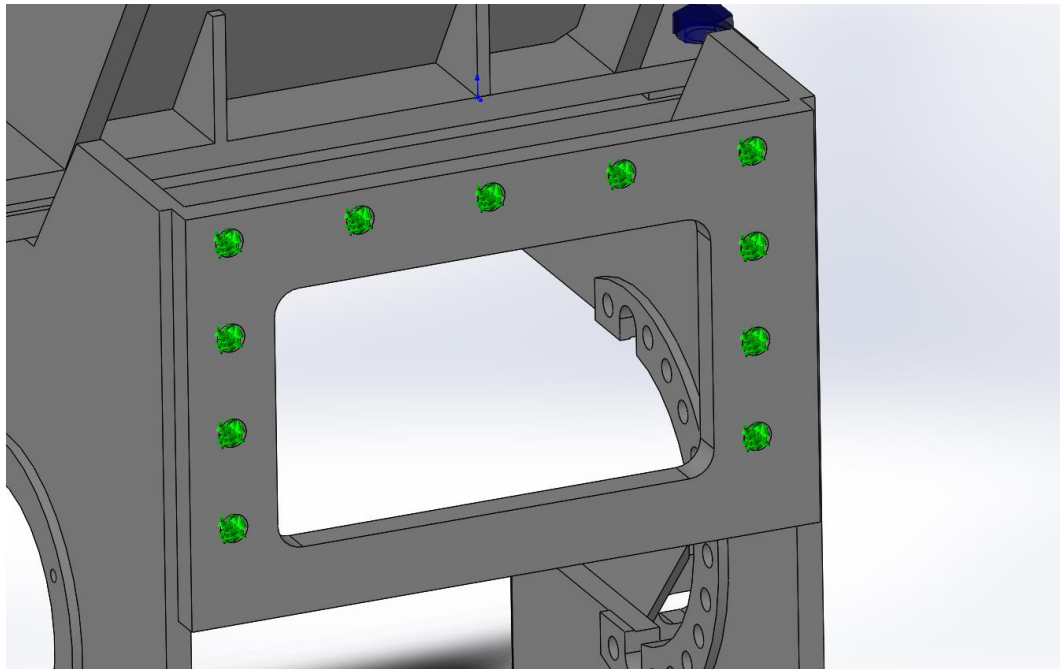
Крепление фланца трубы со стороны портала
